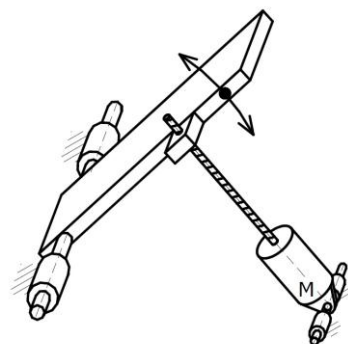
Rotační motor s ozubeným řemenem/řetězem/lankem [2]
